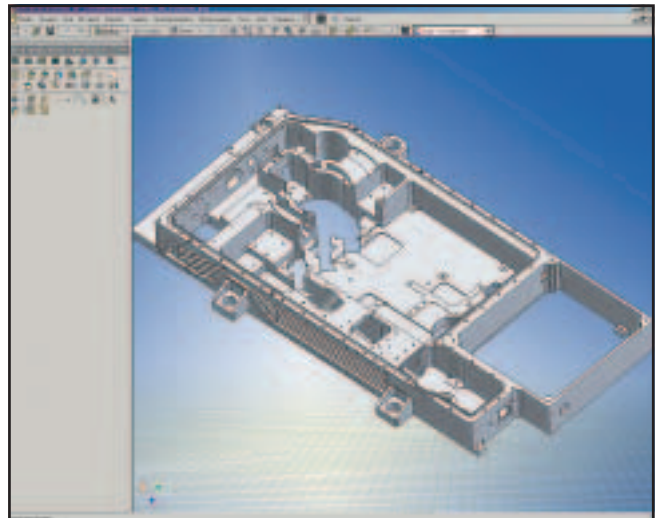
3D-модель корпуса прибора сканирования в Autodesk Inventor
